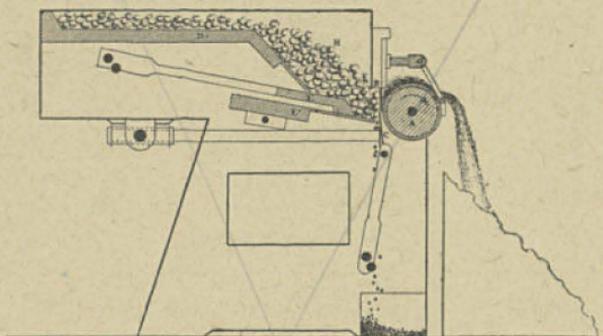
Coupe d'une égreneuse Mac Carthey.
